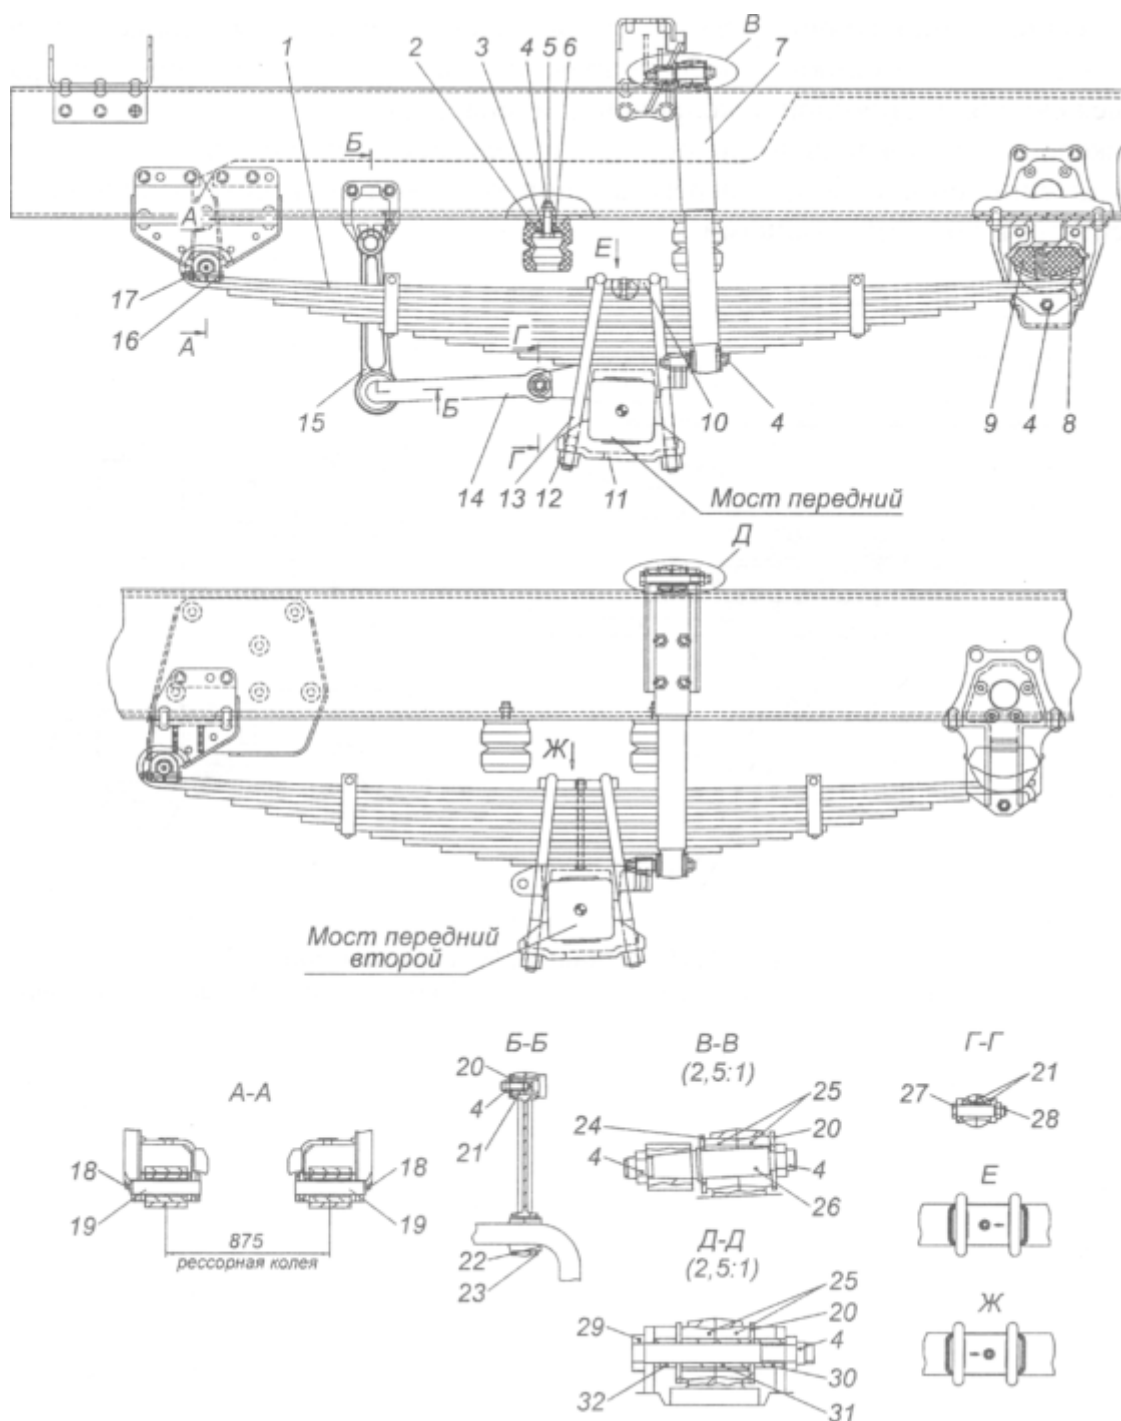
Подвеска передняя: 1 - рессора передняя; 2 - втулка буфера; 3 - проставка; 4 - гайка М16х1,5; 5, 16, 29 - болт; 6 - буфер передней рессоры; 7 - амортизатор; 8 - опора рессоры; 9 - упругий элемент; 10 -
